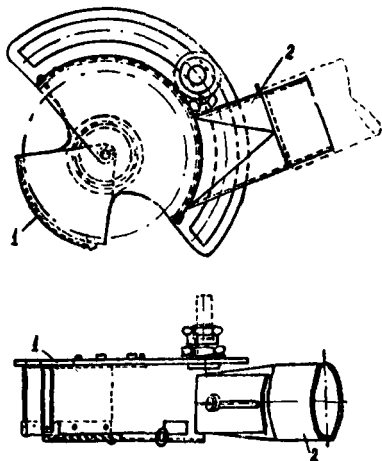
Защитно-обеспыливающий вытяжной кожух для универсально-шлифовального станка:
